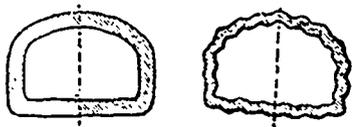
Coupe d'une cornue à surface lisse. Fig. 3. Coupe d'une cornue ondulée de même section.
